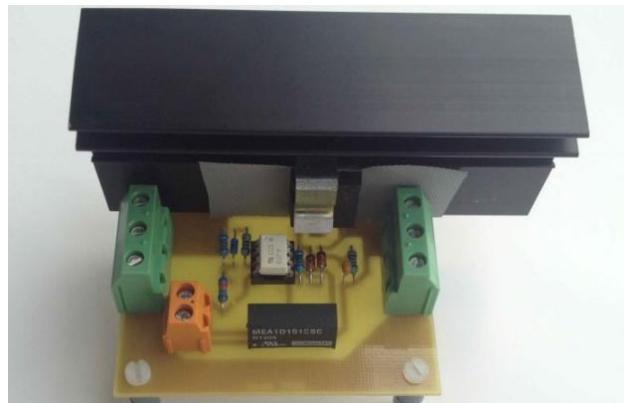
PCB com circuito de proteção do barramento CC para 350 V.
